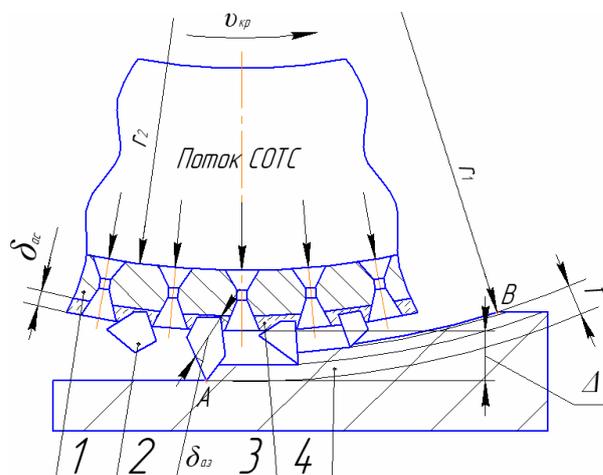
Схема работы алмазного круга: 1 – корпус круга; 2 – алмазное зерно; 3 – связка; 4 – обрабатываемая поверхность детали
